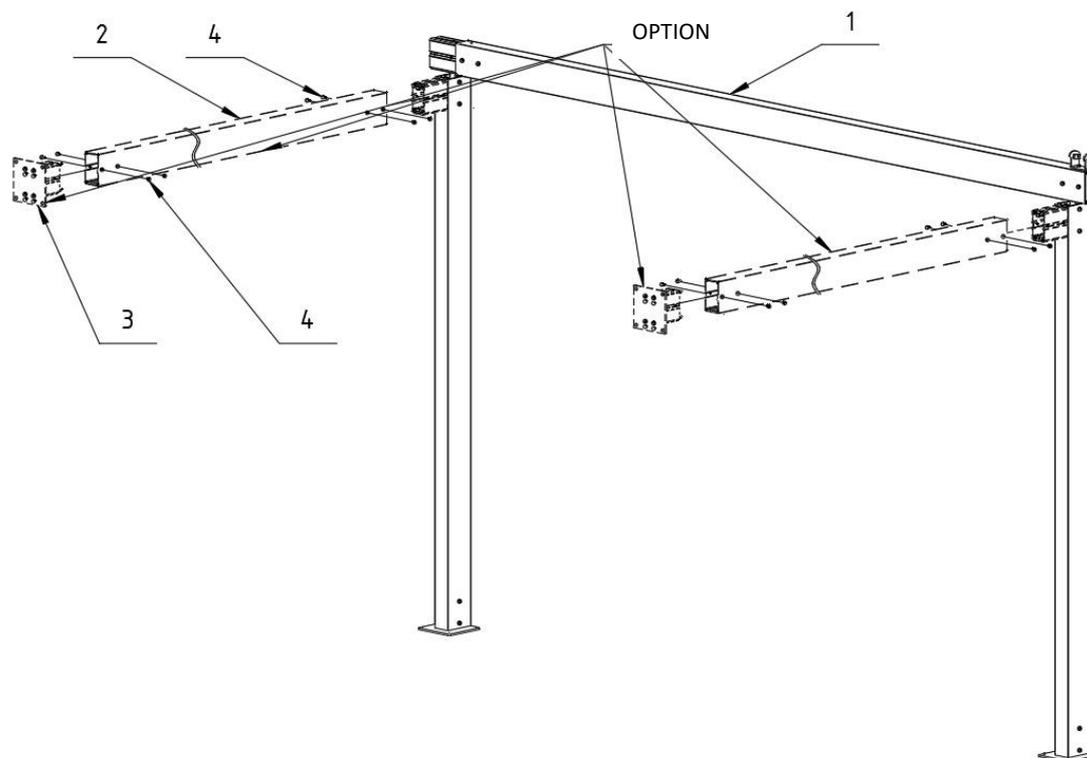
Méthode d'assemblage des poutres latérales dans le premier module : 1 - Module de poteaux hauts, 2 - Poutre latérale, 3 Pied arrière (optionnel), 4 - Boulon M8x16 (optionnel).
